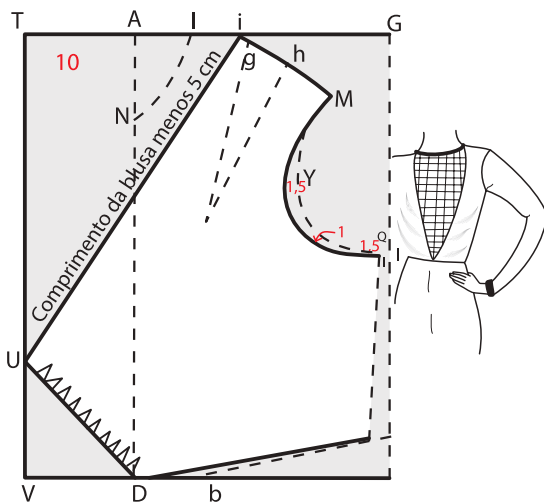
Desenho e molde da blusa drapê- 2º Tipo.
